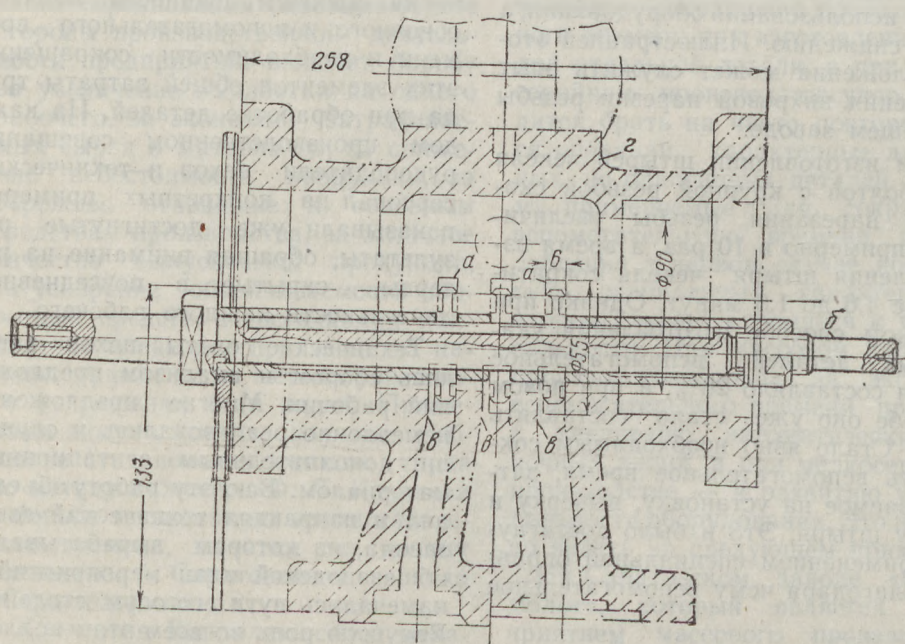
Строенная фреза для обработки паровпускных каналов золотниковой коробки донок типа "Вира":
